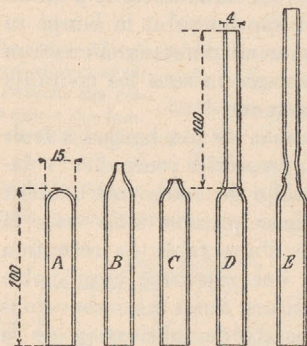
Fabrication d'une ampoule pour tube à vide d'amateur.
